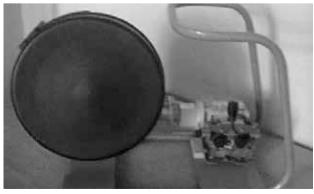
Внешний вид блока (механизма) подачи присадочной проволоки АДЦ 628.04.00.000
